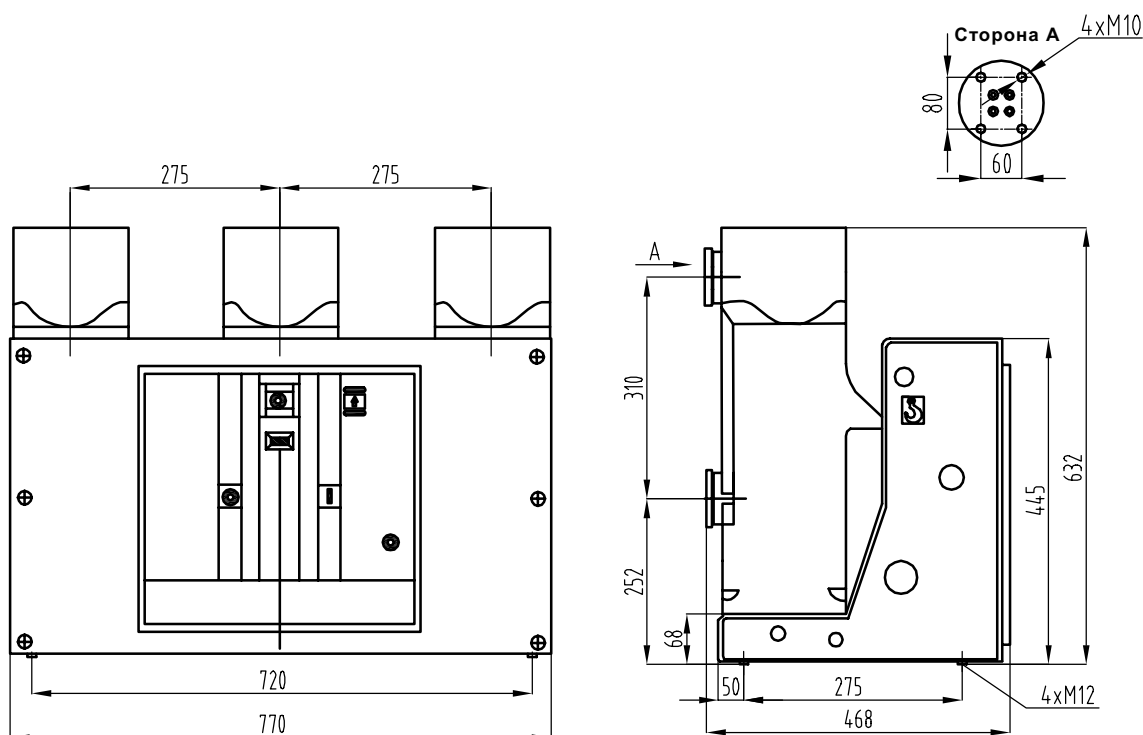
Габаритный размер выключателя ВВ-12 стационарного исполнения для ячейки шириной 1000 мм
